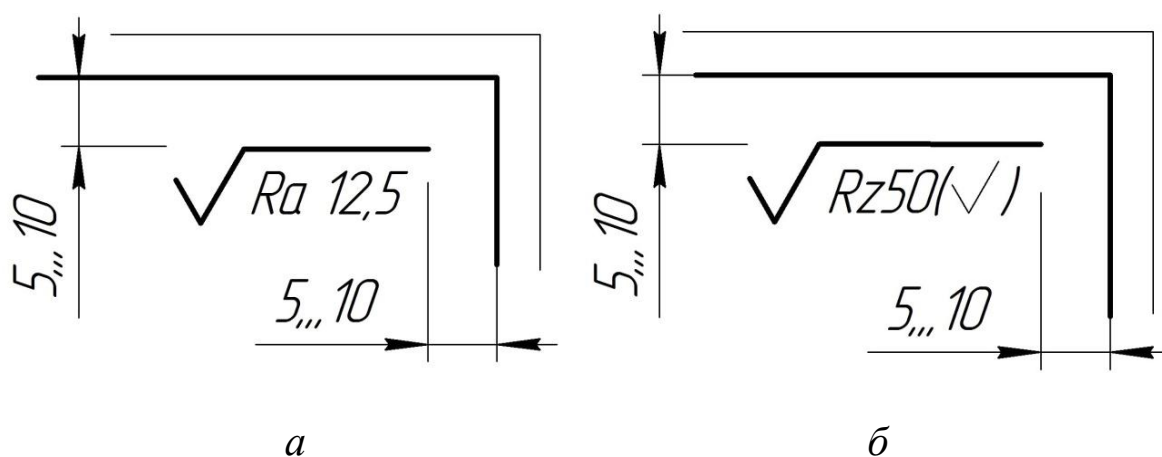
Указание шероховатости, одинаковой для всех или части поверхностей изделия
